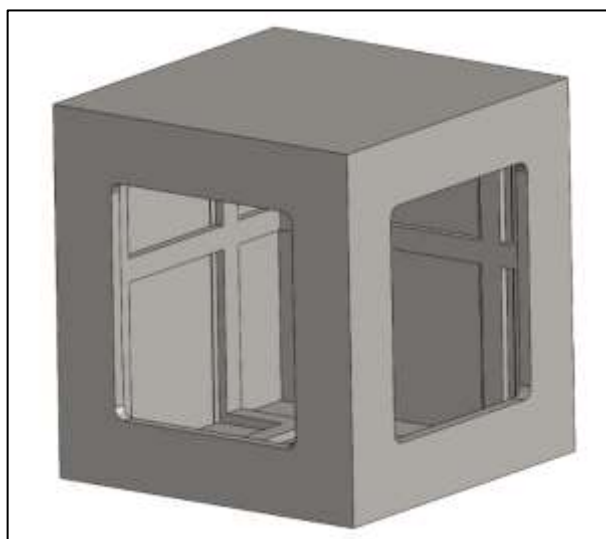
Cámara con plancha de 1.5mm, con refuerzo
